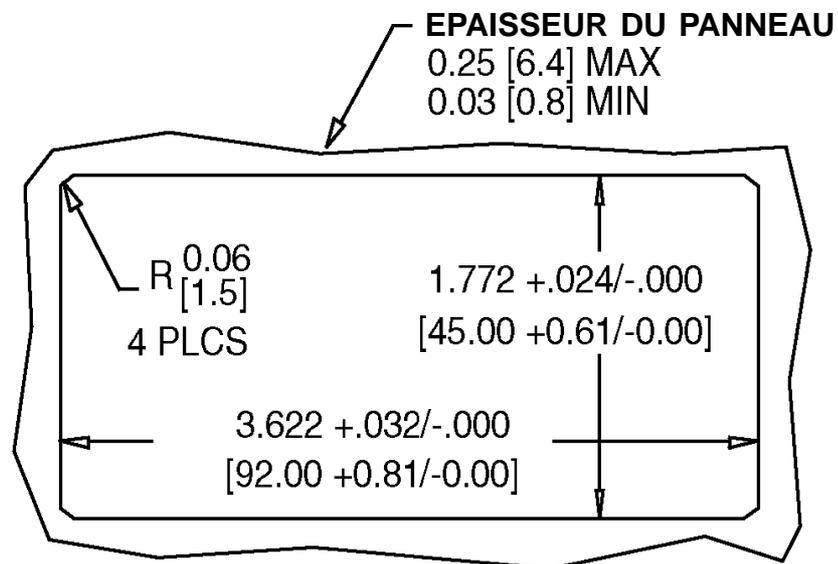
Dimensions du perçage pour montage panneau en pouces (en millimètres entre parenthèses)
